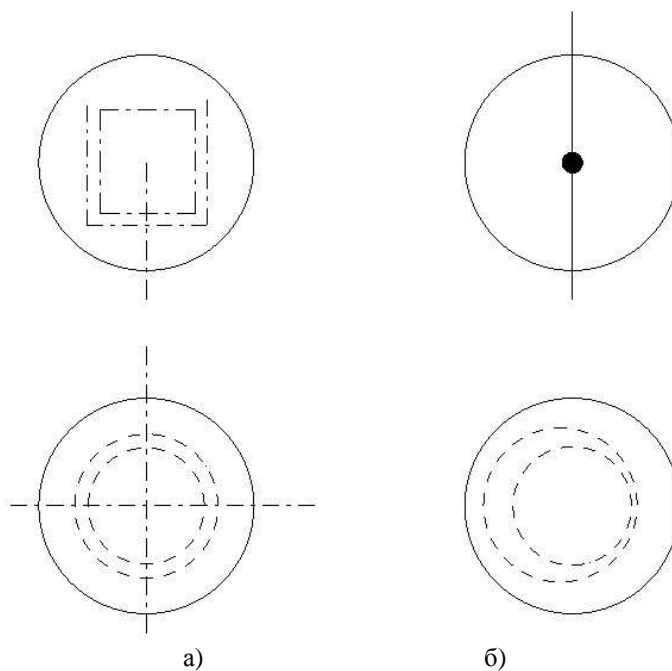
Схема поперечного расположения неметаллических включений после прошивания трубной заготовки полученной на установке непрерывного литья:
